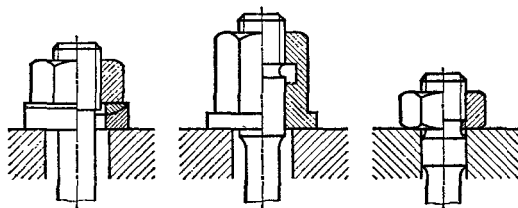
Способы конструктивной разгрузки резьбы от изгиба
